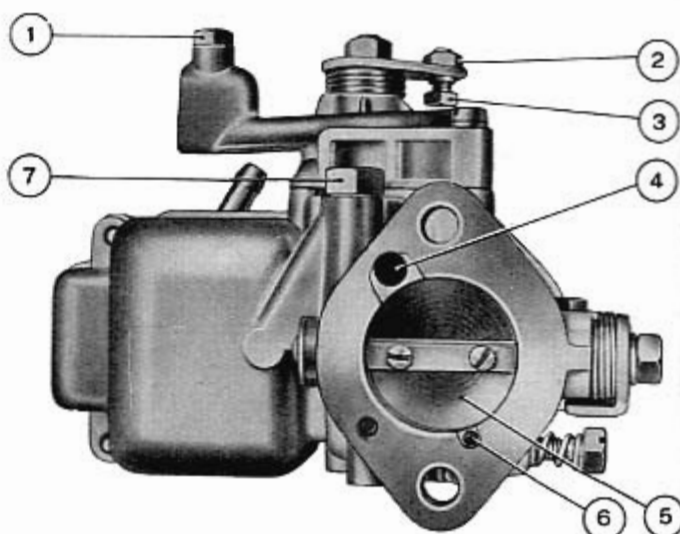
Carburateur Weber 26 IMB 1, vu d'en bas.
